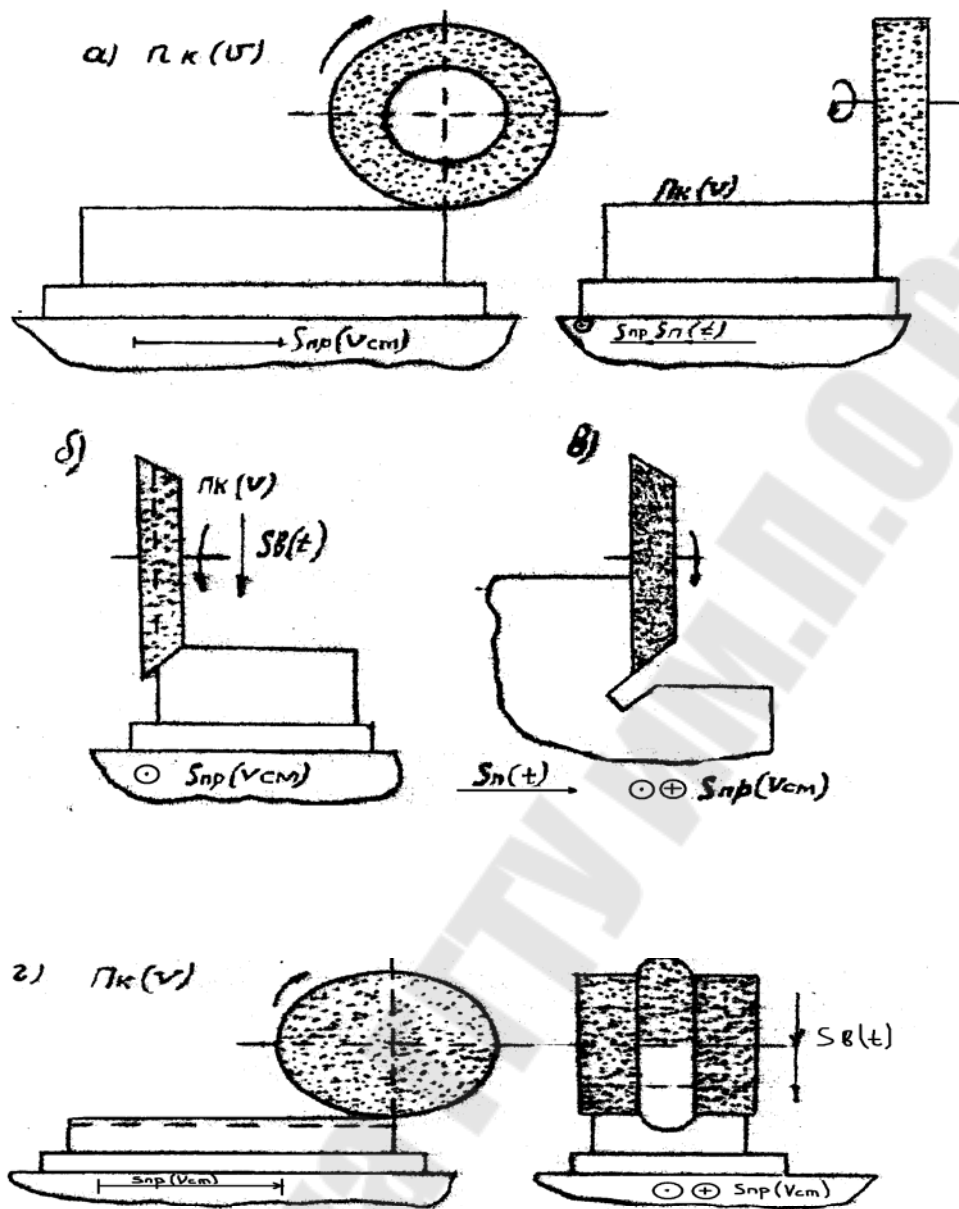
Закрепление инструмента и схемы обработки заготовок на плоскошлифовальных станках.
